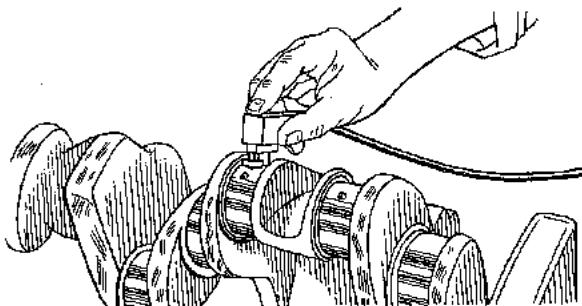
Comprobación del acabado superficial sobre la máquina (Micrometrical Manufacturing Co.)
